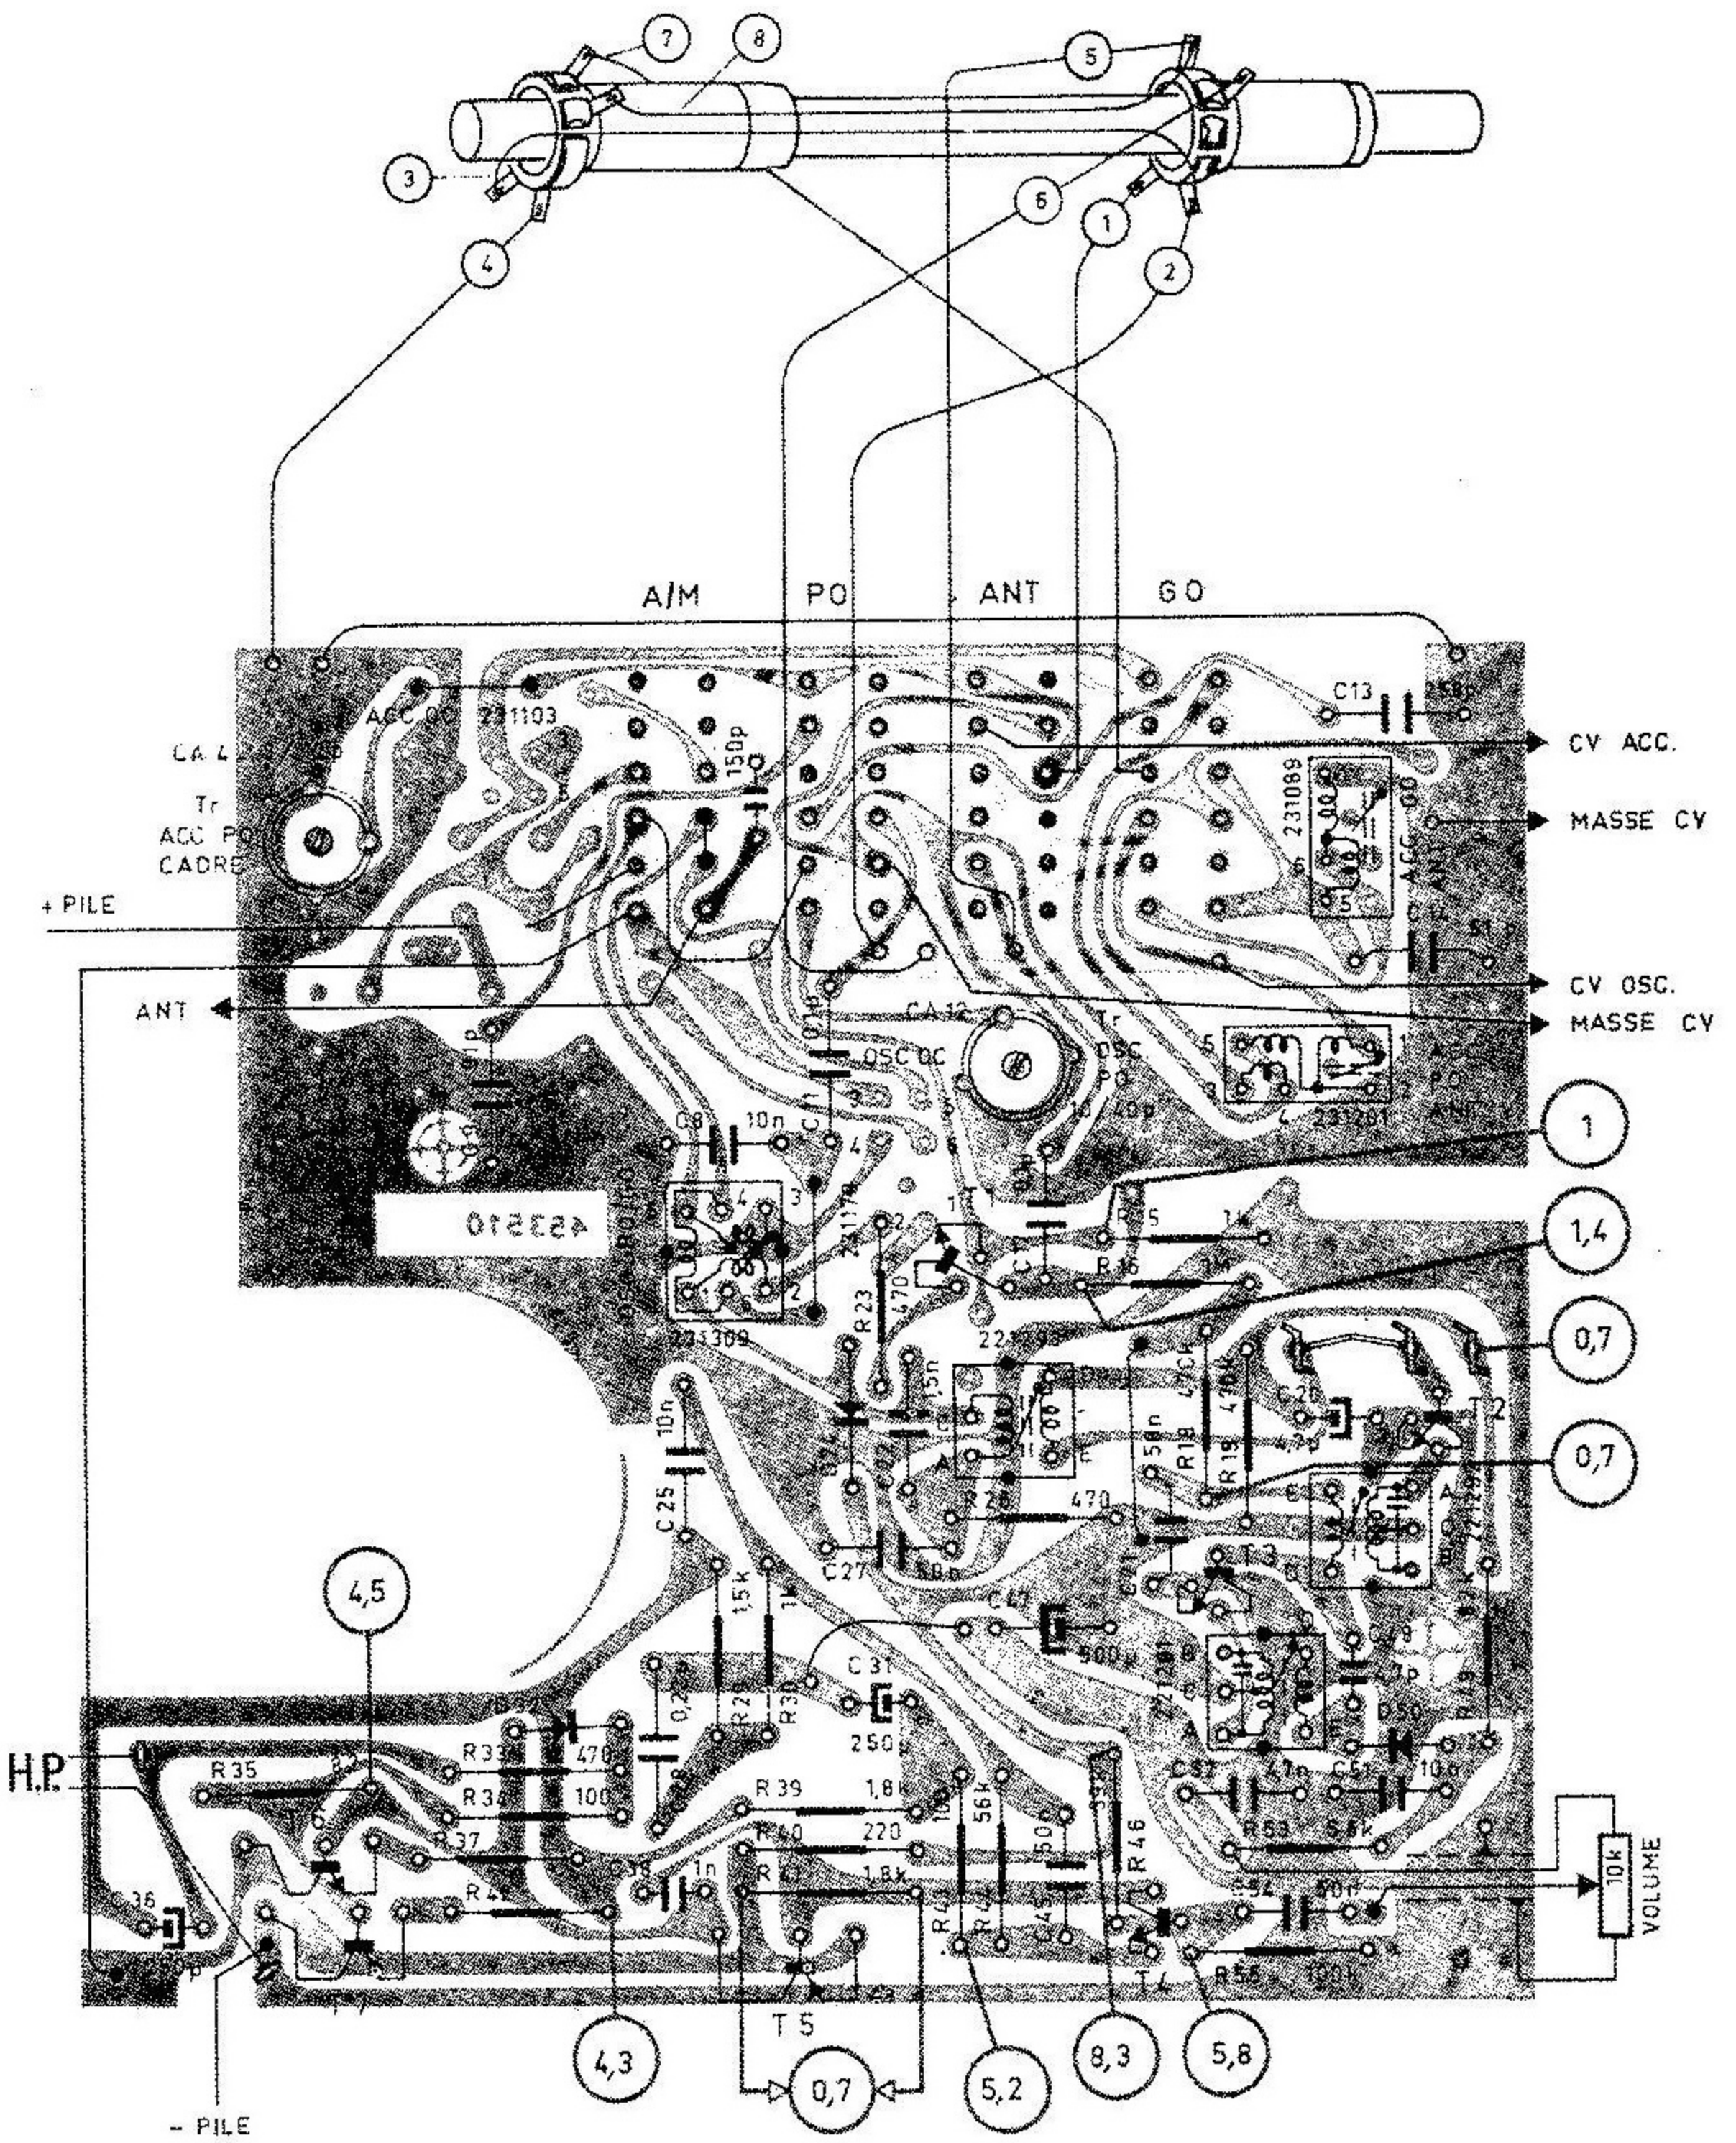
Platine imprimée vue côté composants, avec l'indication des principales tensions.
